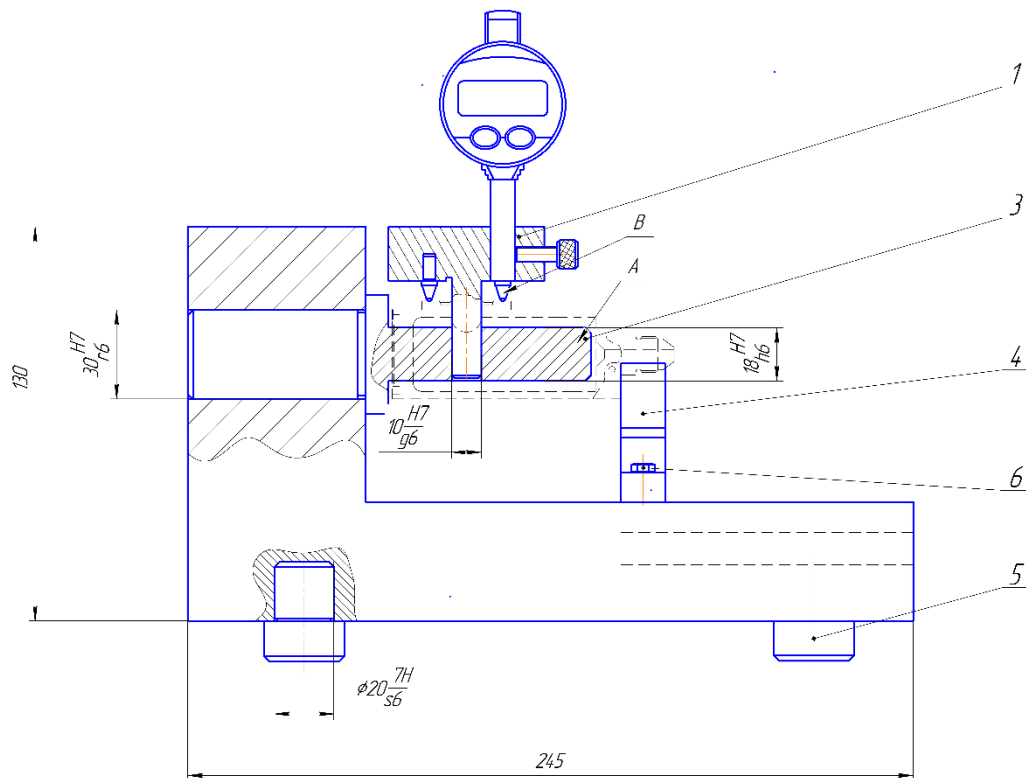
Контрольно-измерительное приспособление вид спереди
